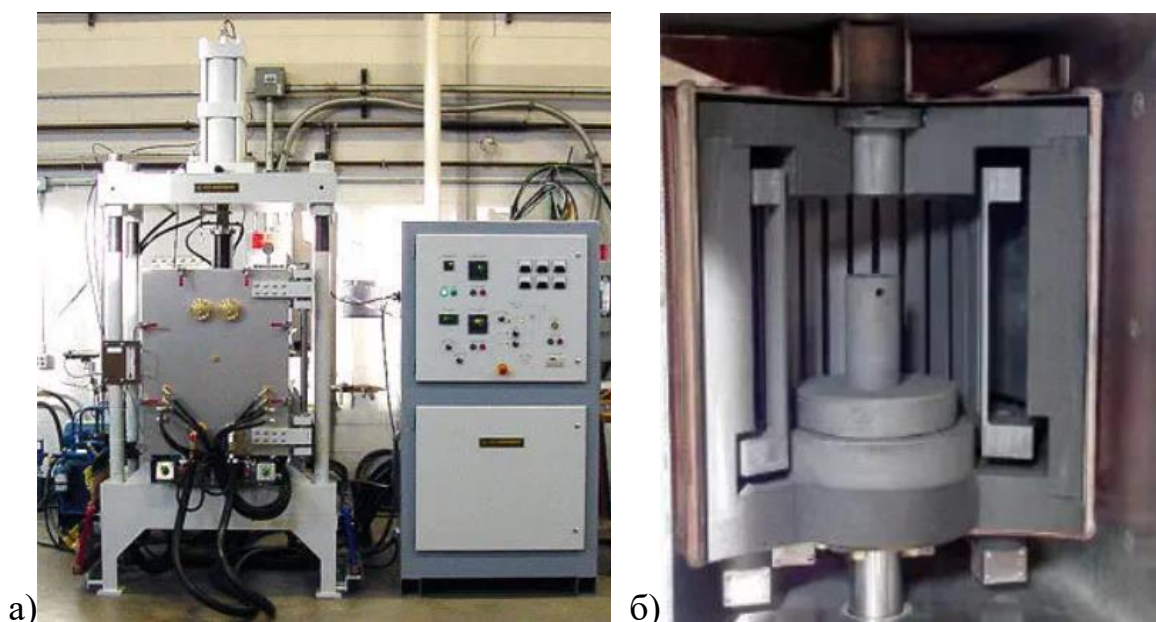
піч гарячого пресування: а – установка печі з шафою керування; б – робоча камера печі з рухомим штоком, який прикладає навантаження до заготовки, протягом спікання;
